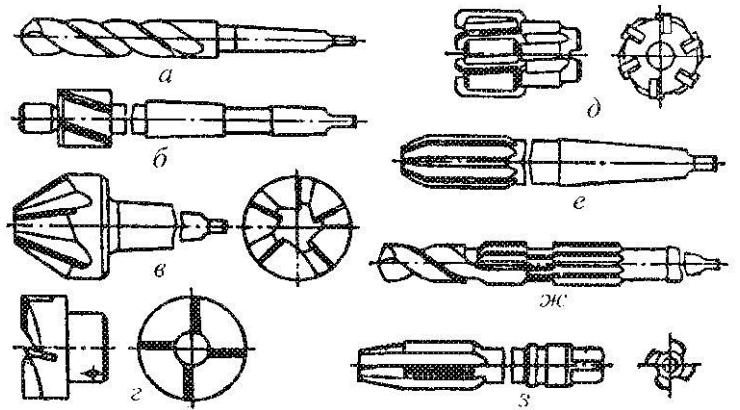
Інструменти для обробки отворів на свердильних верстатах
